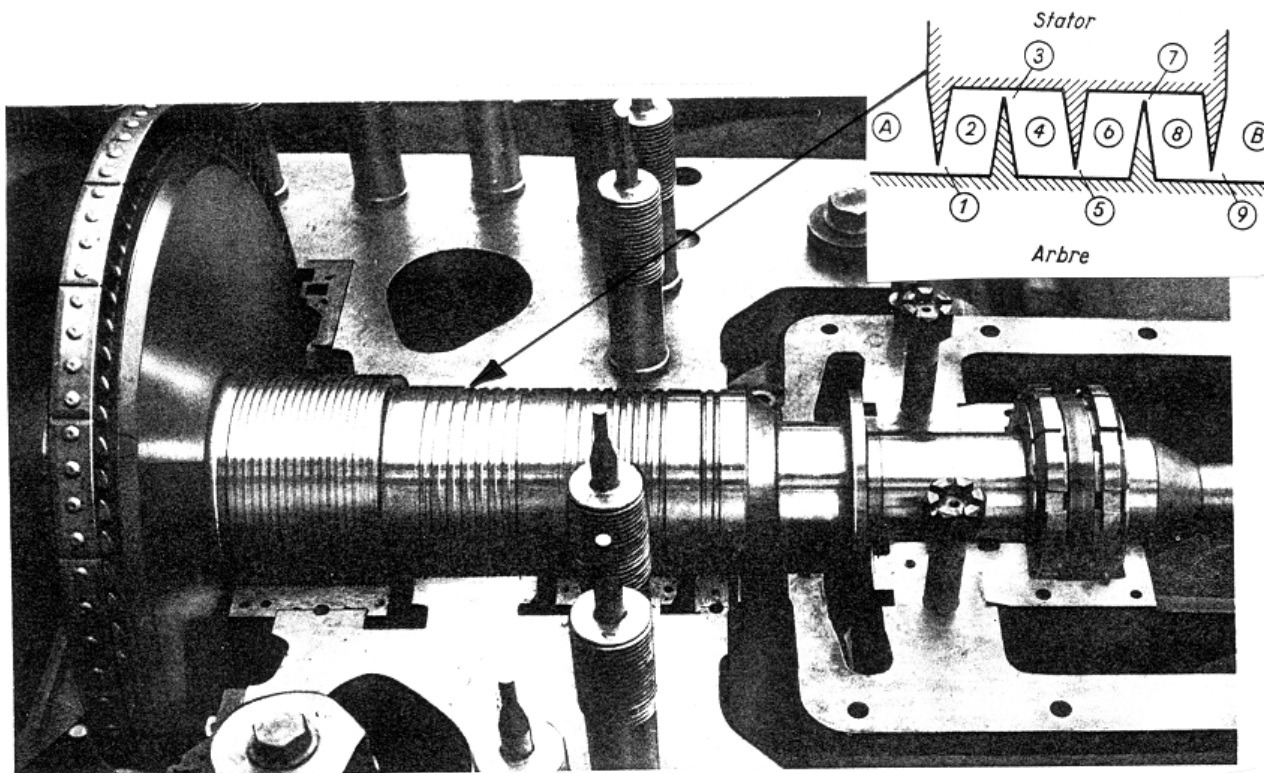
Dispositif d'étanchéité vers l'extérieur de type labyrinthe [9]
